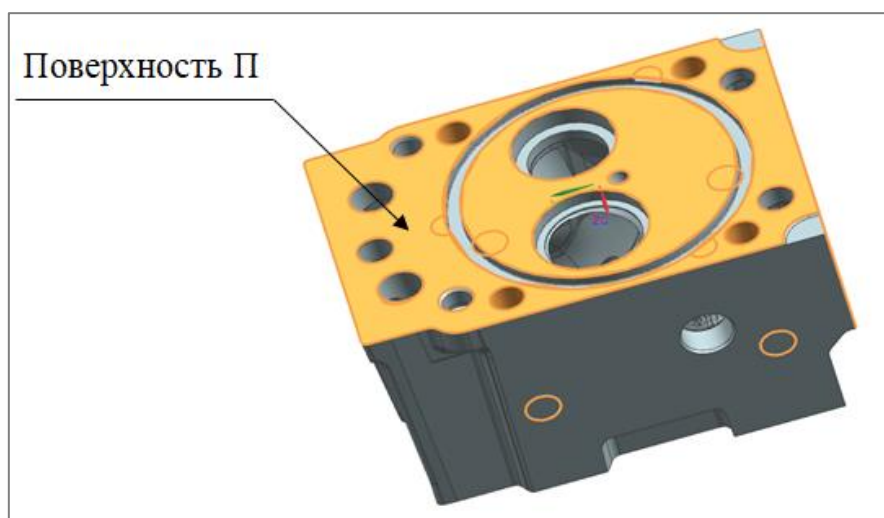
Привалочная поверхность П головки цилиндра двигателя КАМАЗ
